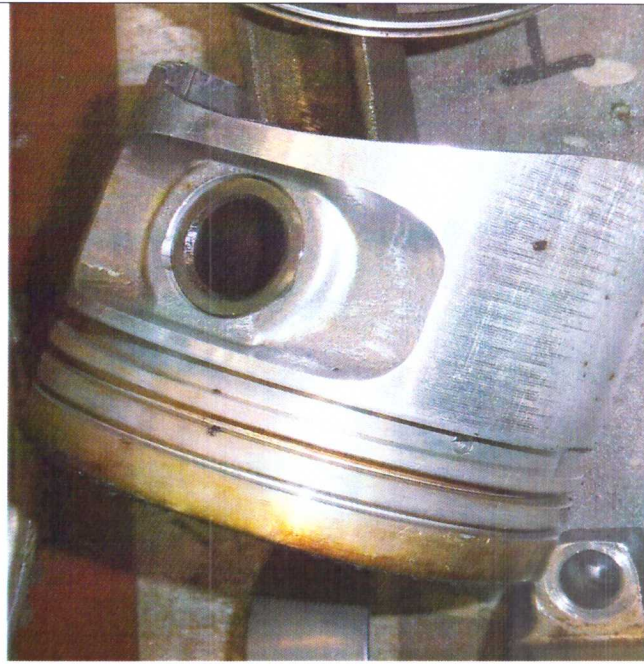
Внешний вид боковой поверхности поршня третьего цилиндра по окончании длительных испытаний двигателя при работе на базовом масле Castrol EDGE
